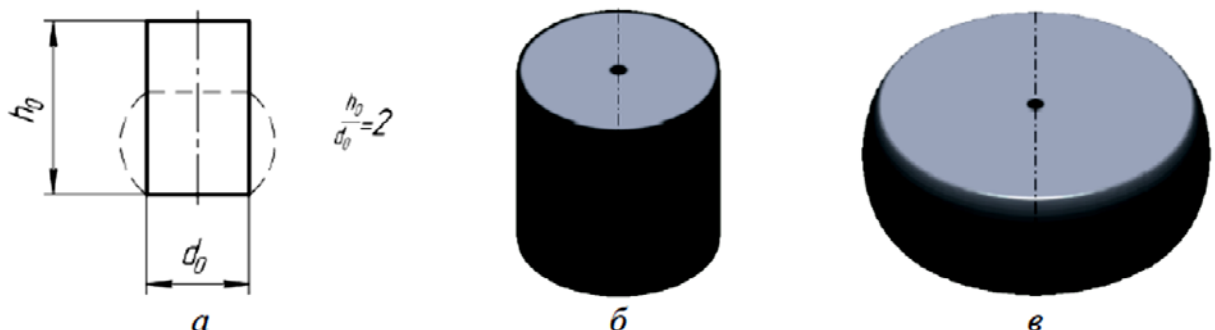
Проба на осадку: а – схема испытания; б – образец до испытания; в – образец после испытания
